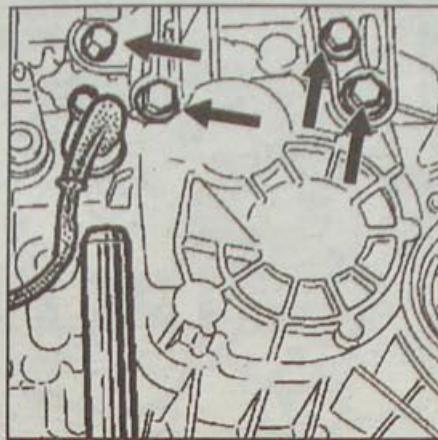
Расположение болтов крепления левой опоры коробки передач
